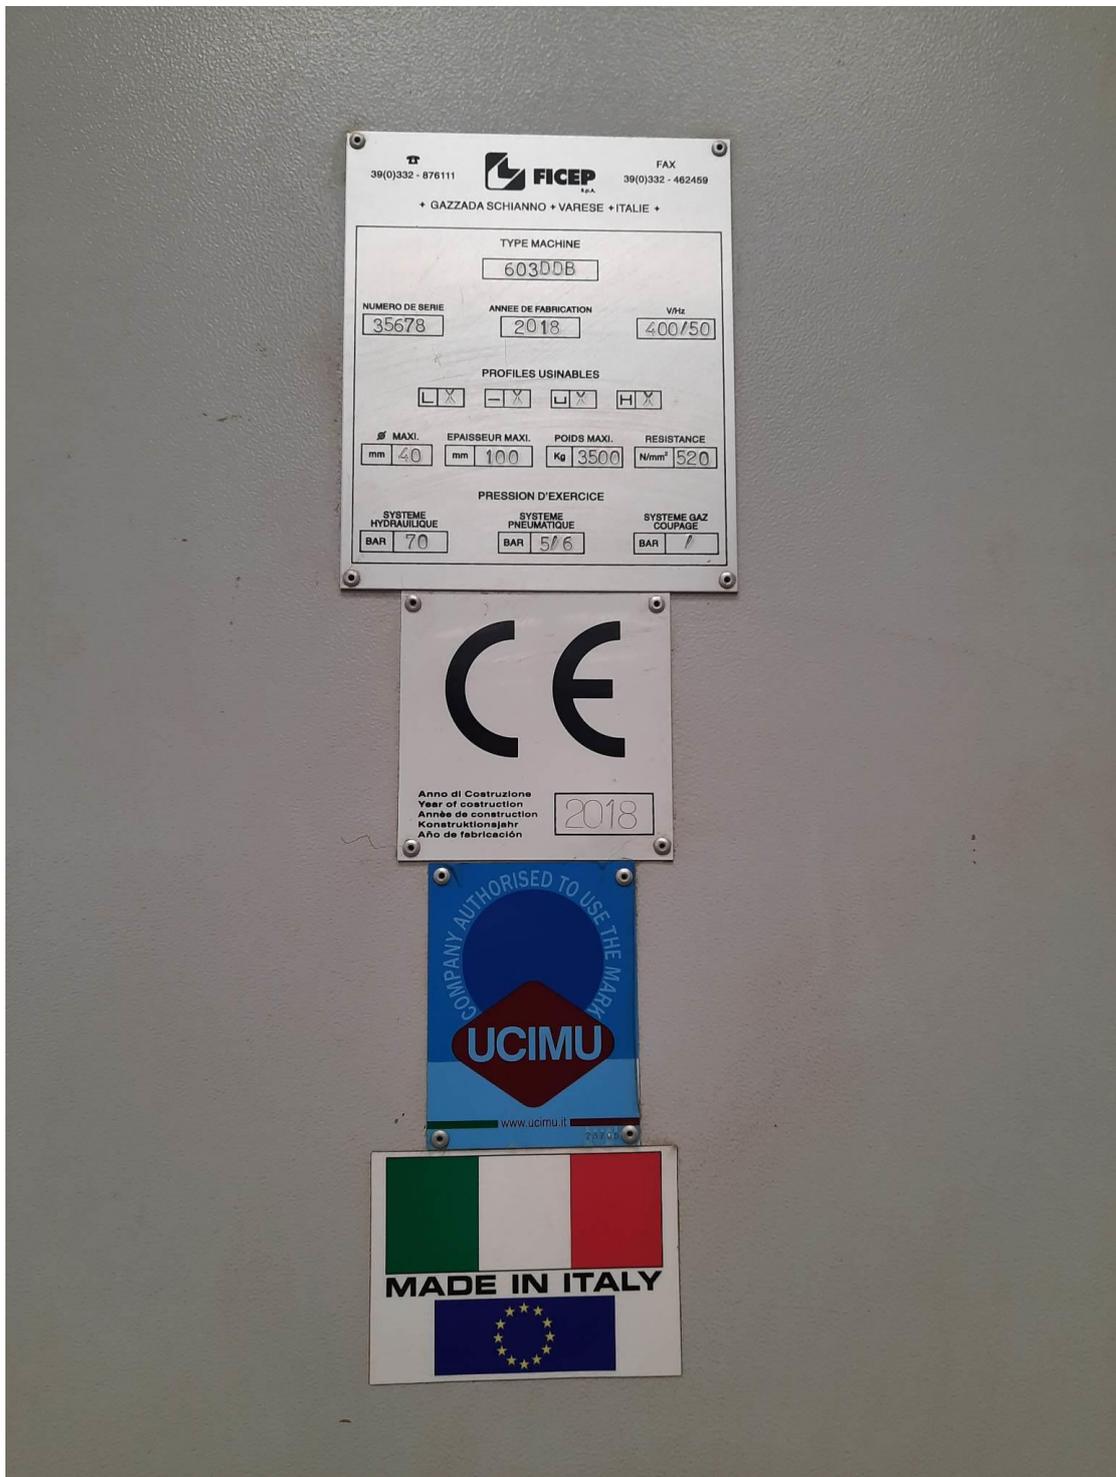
4 Image réelle de la Plaque significatif de la machine « 603 DDVB »
